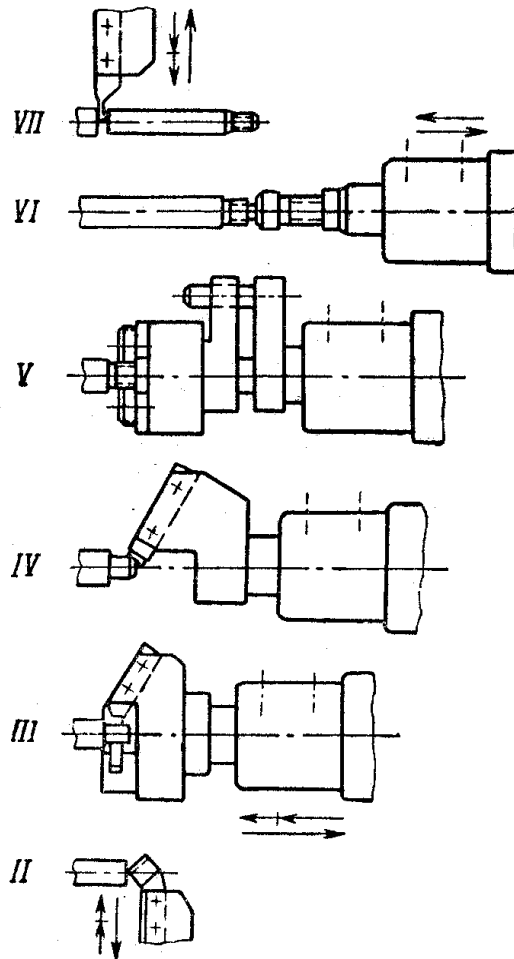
Технологічна схема валів на токарно-револьверному верстаті:
